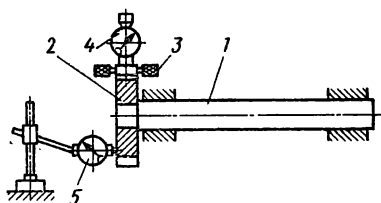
Схема проверки зубчатого колеса на радиальное и торцовое биения:
